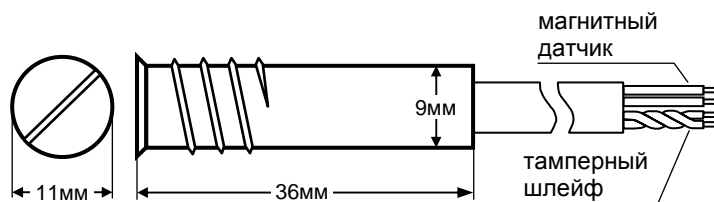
Геркон извещателя S-3 в металлическом корпусе
